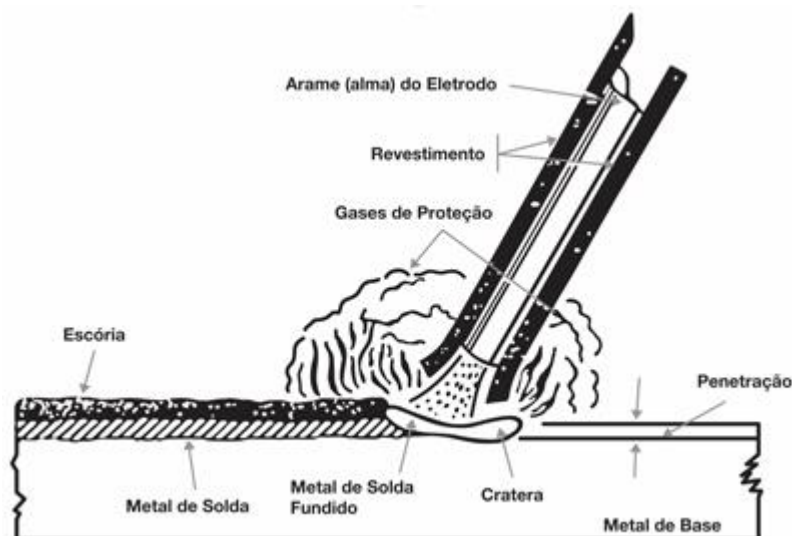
Ilustração esquemática do processo de soldagem por eletrodo revestido
